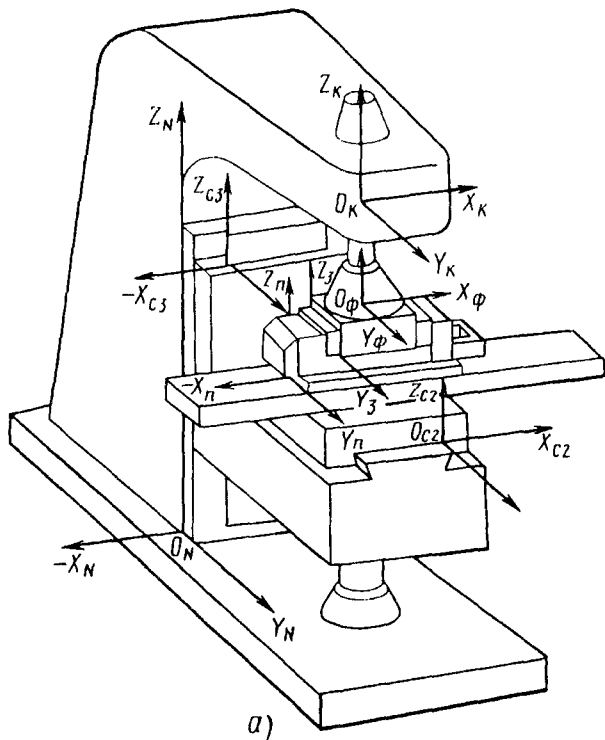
Вертикально-фрезерный станок (начало рисунка).
